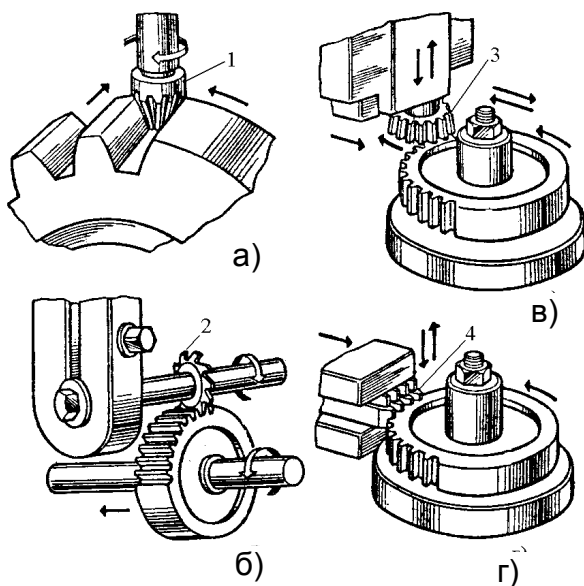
Виготовлення зубчастих коліс копіюванням за допомогою фрез (*а* і *б*) та обкочуванням за допомогою довбача і гребінки (*в* і *г*): 1 – пальцева фреза; 2 – дискова фреза; 3 – довбач; 4 – гребінка
